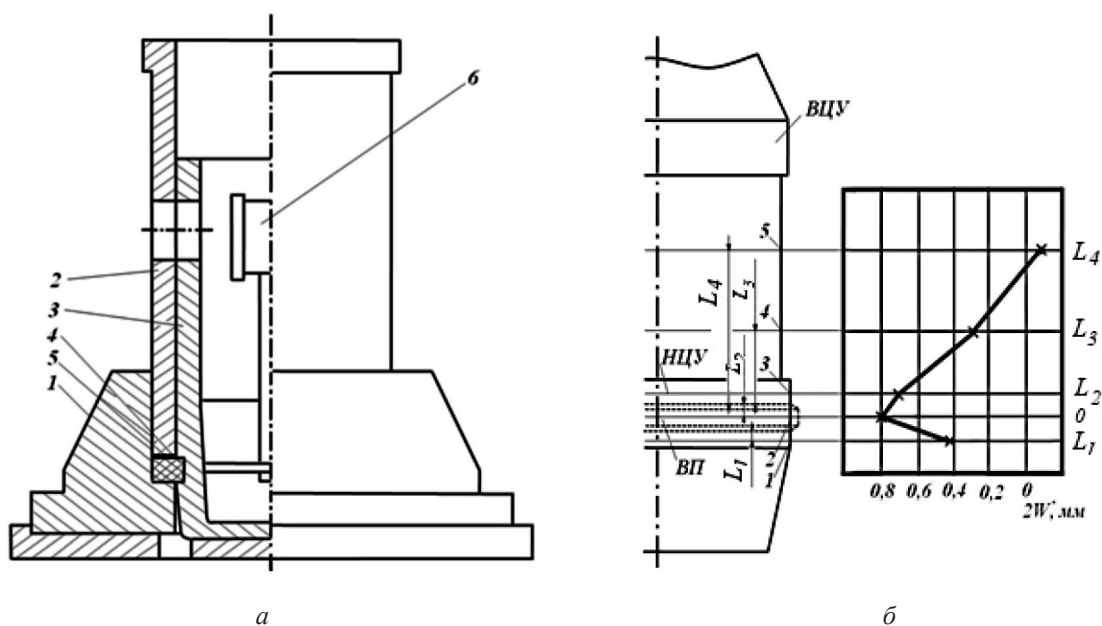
Схема установки для локального кольцевого нагружения корпуса АС среднего калибра в зоне ВП (а) и результаты измерений с ее помощью (б): 1 — матрица; 2 — полый пуансон; 3 — исследуемый корпус; 4 — рабочий объем (цереин); 5 — свинцовые прокладки; 6 — индикаторный измеритель
